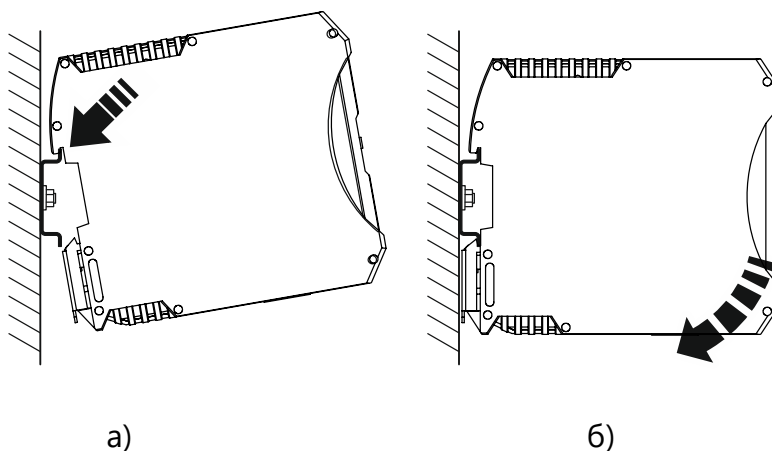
Установка АСМ-IP3 на DIN-рейку
